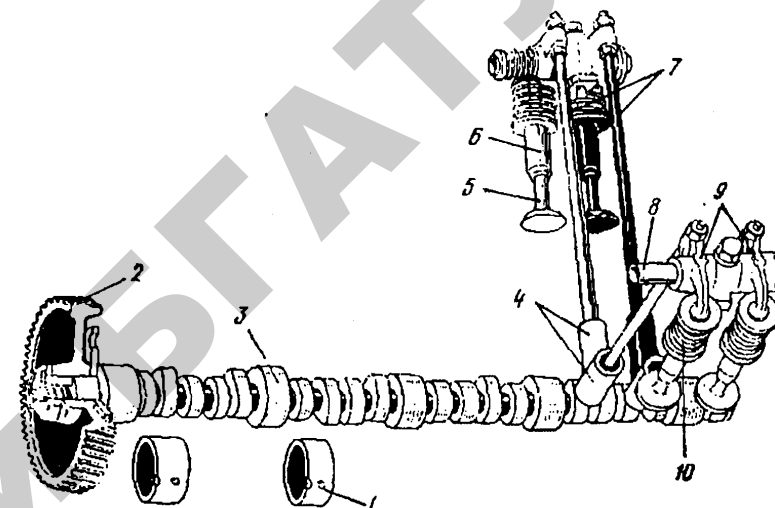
Газораспределительный механизм V-образного двигателя
